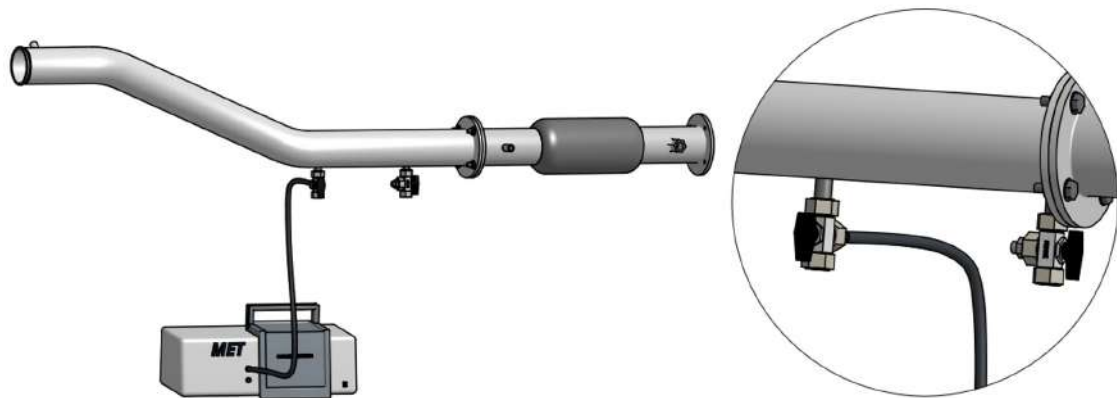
Dibujo CAD de la adaptación al escape del motor.
